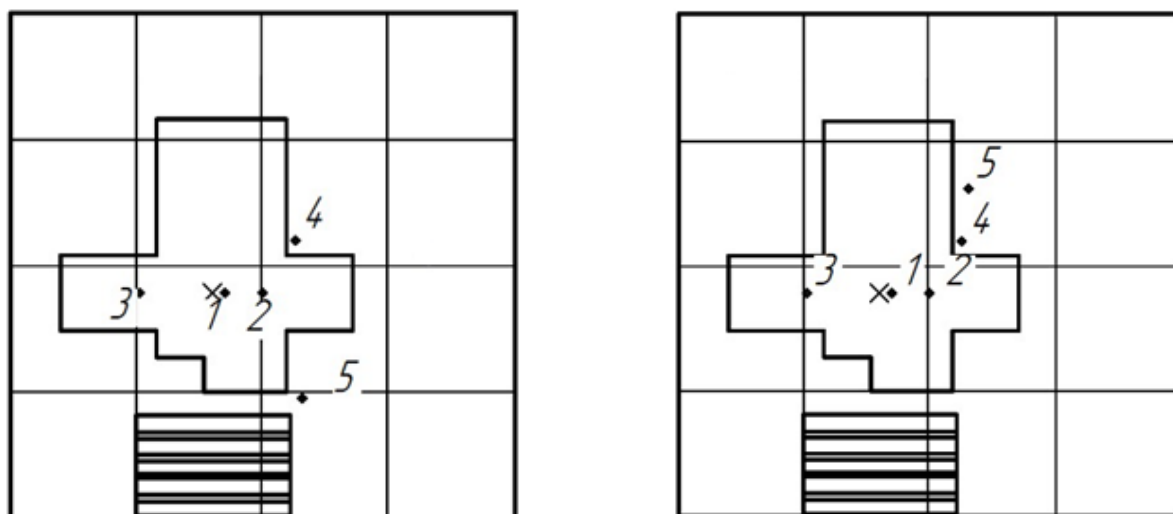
Положение контрольных точек для сбора пыли: от станка вертикально-фрезерного 6А12А – слева и от станка консольно-фрезерного вертикального 6Р13 – справа.
